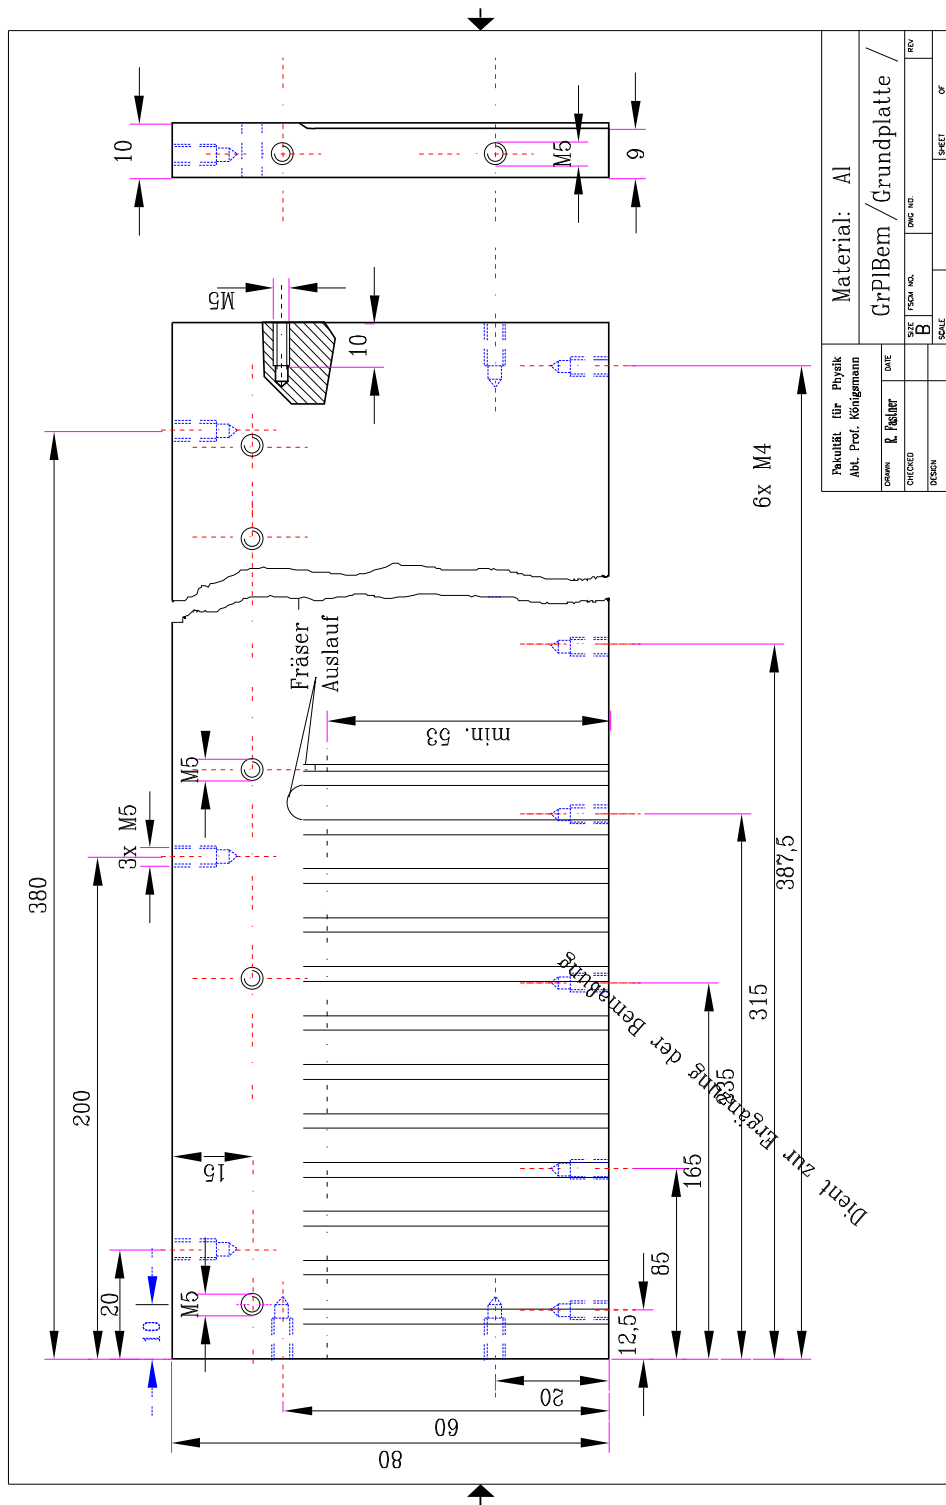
Grundplatte, Zeichnung mit weiteren Bemaßungen.
